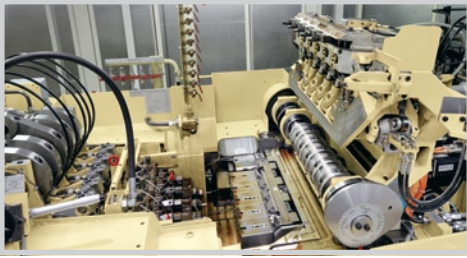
Vorbereiteter Werkzeugblock. Bilder oben: Blick in den Werkzeugraum der AKP 4-5.
